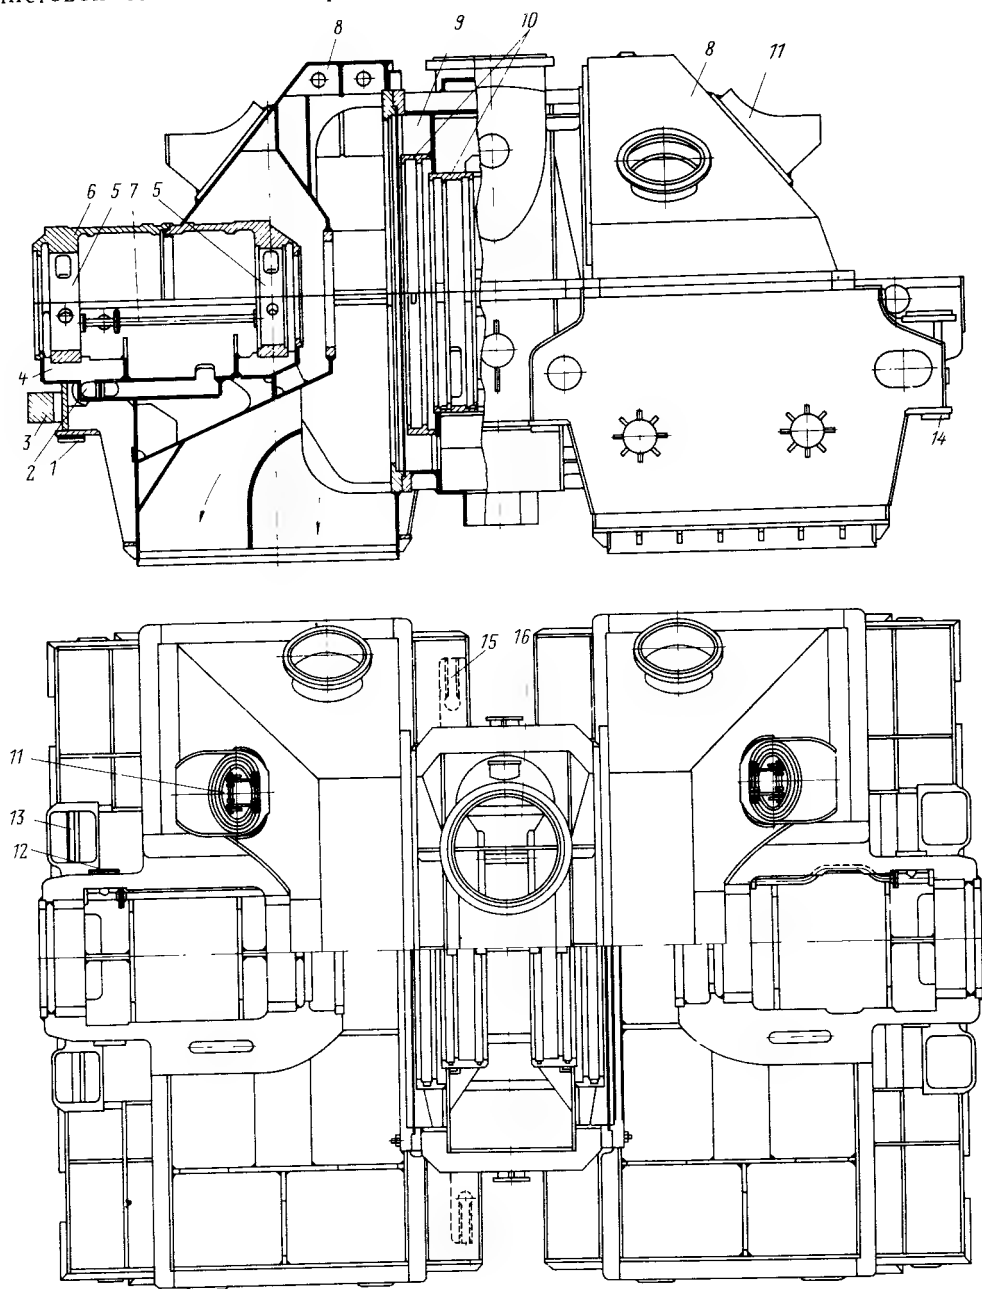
Конструкция одностенного корпуса ЦНД
